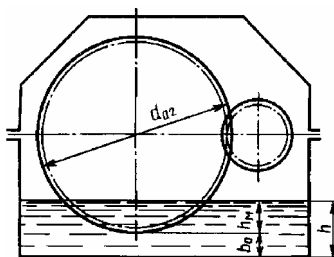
Смазка погружением в цилиндрическом редукторе
